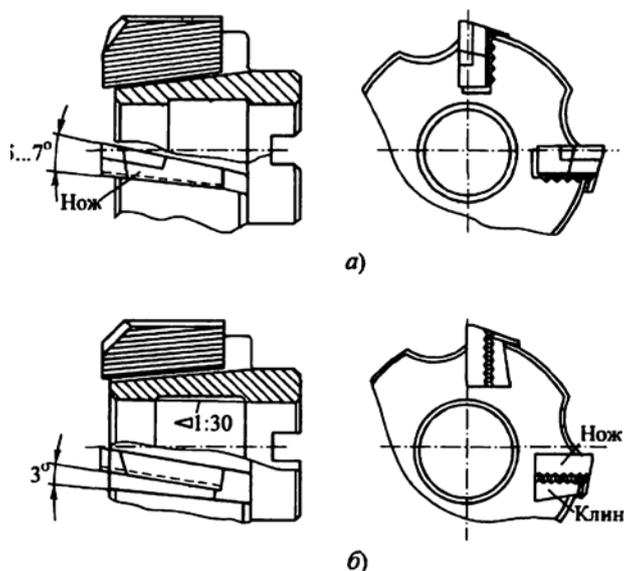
Типы крепления ножей сборных зенкеров:
